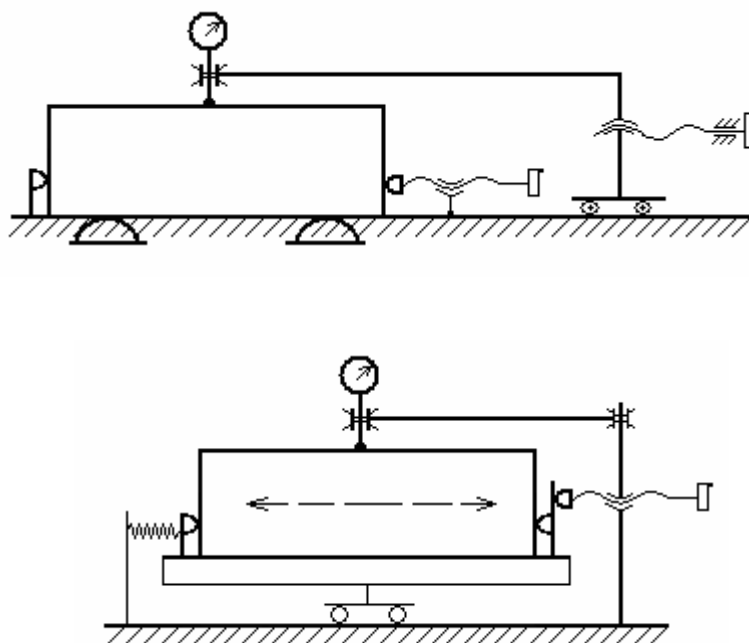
Подвижный и неподвижный кронштейны
